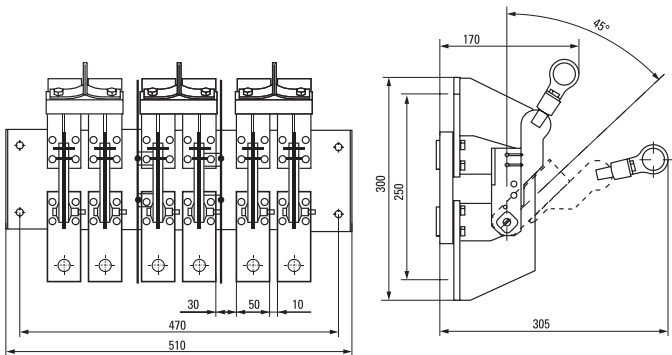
Габаритные и установочные размеры разъединителя типа PE19-44/46 с рычагом для полюсного оперирования штангой
